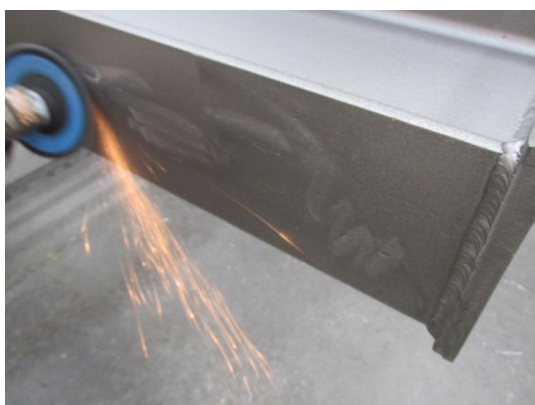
Rebarbagem e retificação de superfície com defeitos
